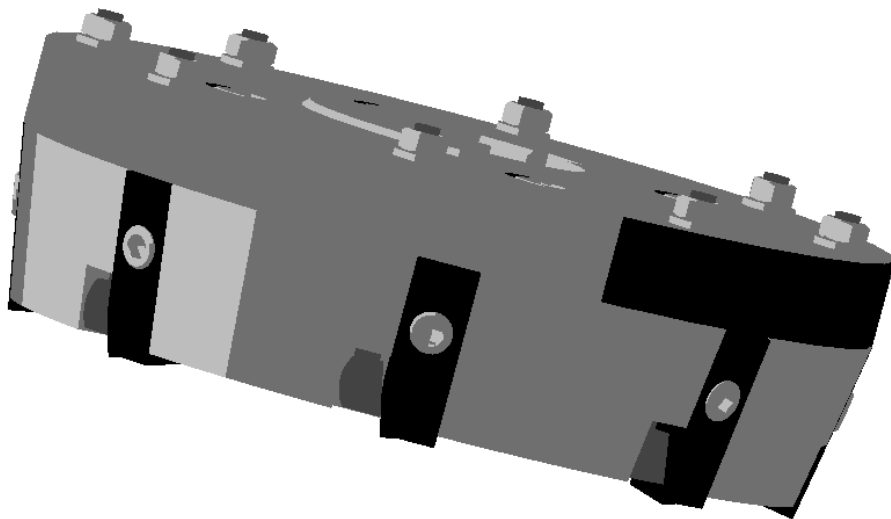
Конструкція збірної торцевої фрези з механічним кріпленням пластини клином
